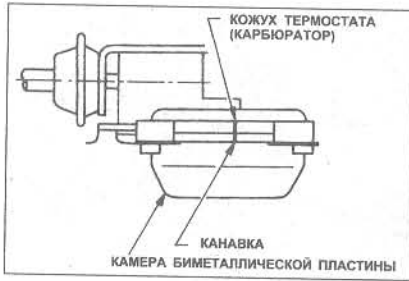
Метки выравнивания карбюратора и покрытия биметаллической пластины (Глава 17)
